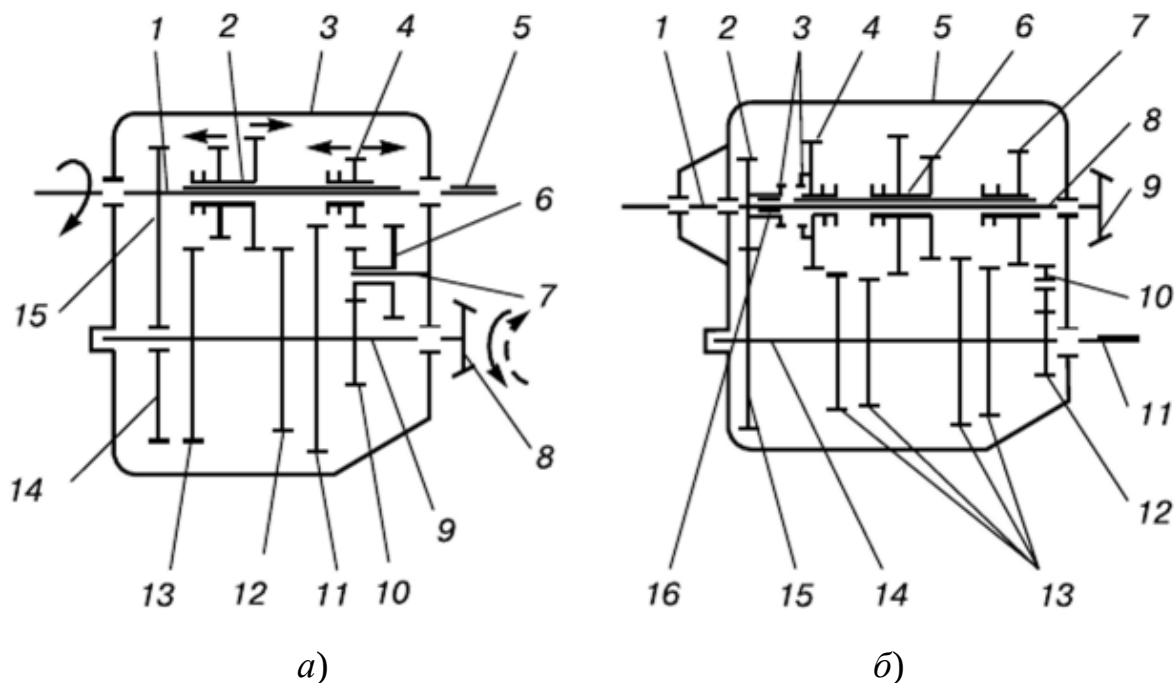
Принципиальные кинематические схемы коробок передач:
